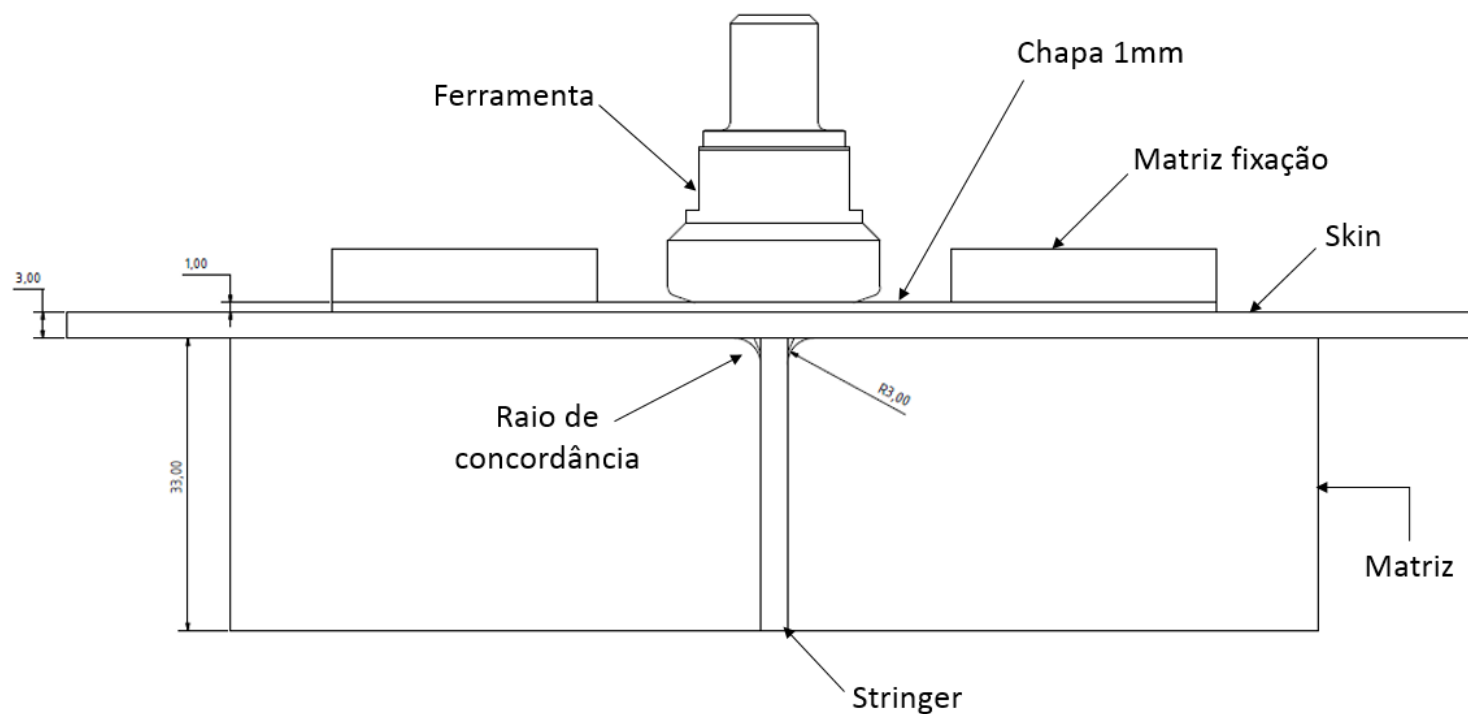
Esquema do equipamento e da montagem usada para a soldadura das juntas T na configuração *T-Lap*..
